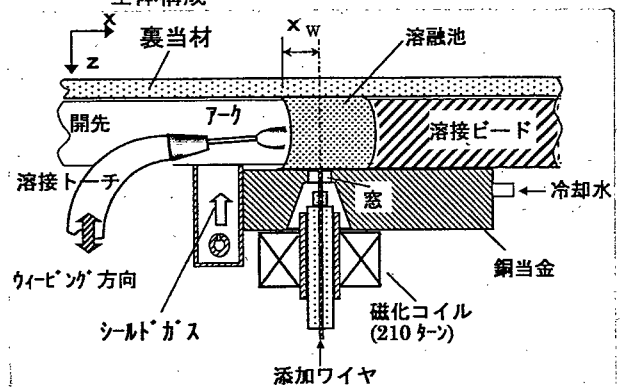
溶接部近傍の機器配置 (開先部の平面視)
